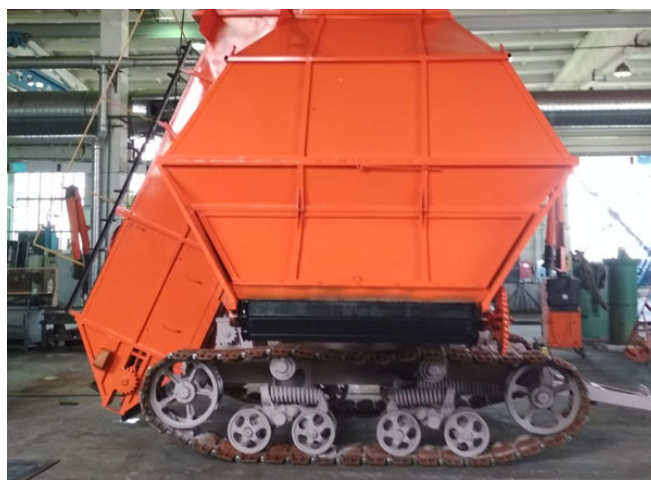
Машина для уборки фрезерного торфа МТФ-43А-МГ
